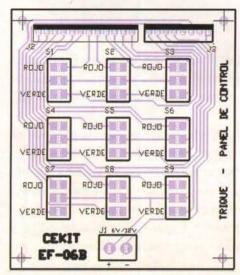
Guía de ensamblaje y circuito impreso del panel de control
